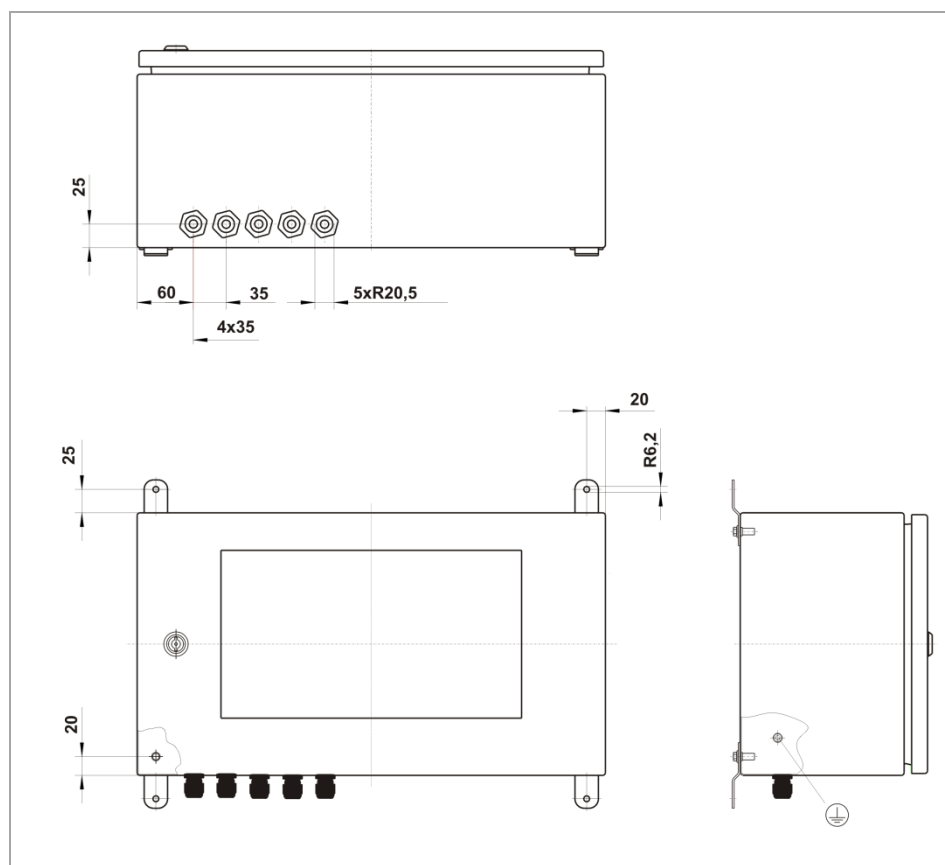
Wandmontage - Abmessungen Befestigungslaschen
